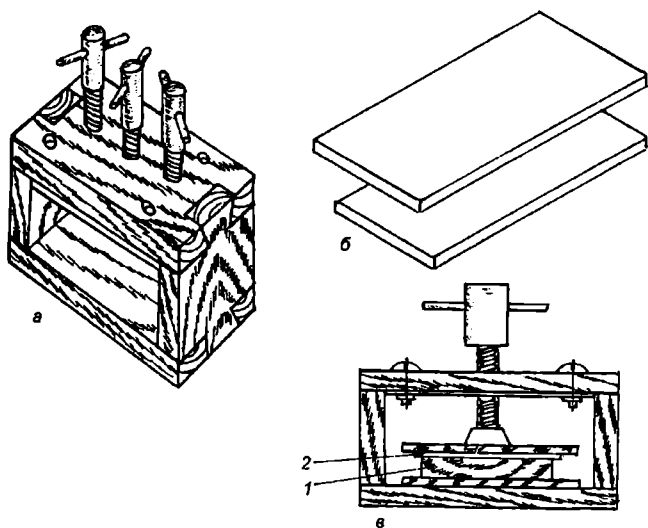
Пресс для наклеивания шпона с запрессовкой:
